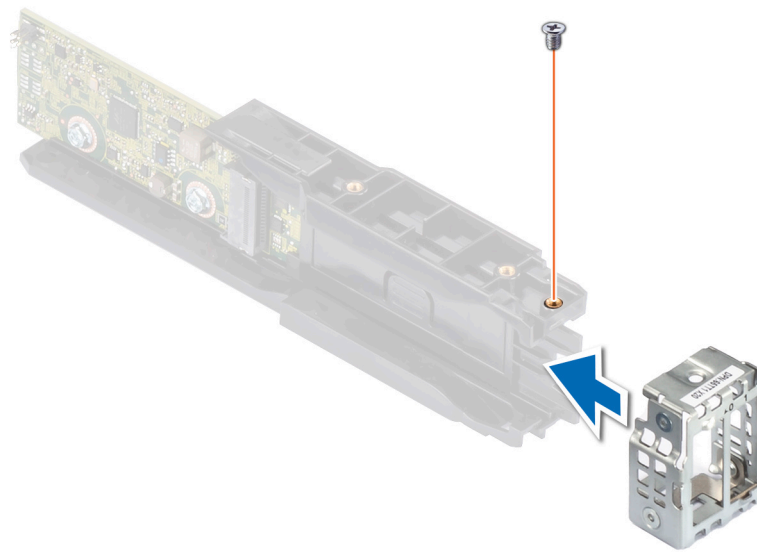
Instalación de la cubierta del módulo de BOSS
